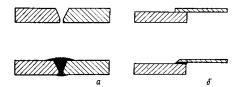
Схема образования шва при пайке-сварке: а – без оплавления кромок деталей; б – с оплавлением кромок одной детали.
